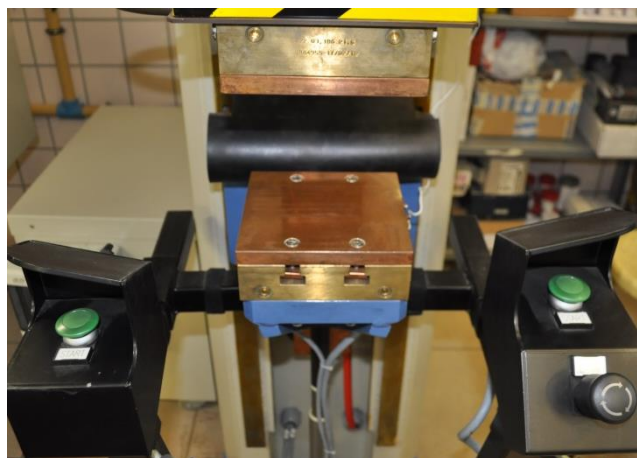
Bancadas de la máquina de soldadura con las placas de cobre incorporadas a las plataformas superior e inferior, con sus tornillos fijadores.
